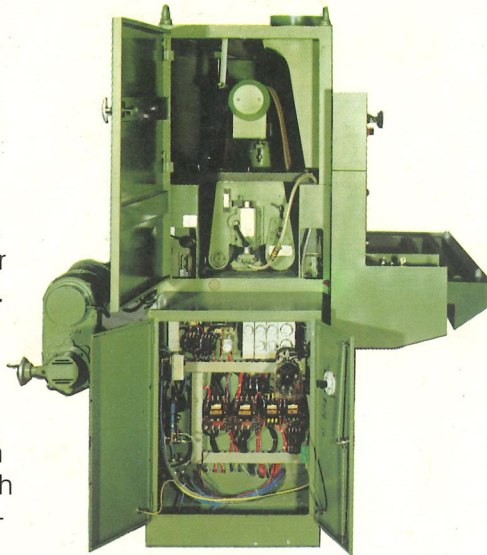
Seitenansicht mit Schleifaggregat und Elektroschaltschrank
